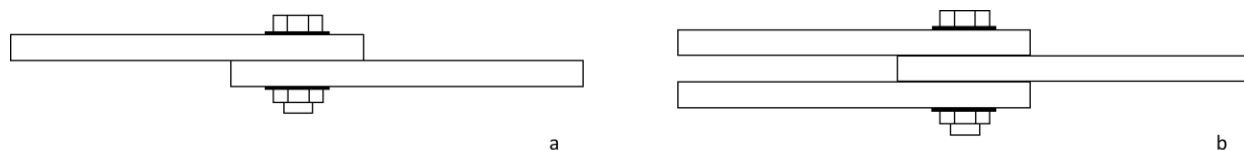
Configuration de joints boulonnés : (a) Simple recouvrement - (b) Double recouvrement
